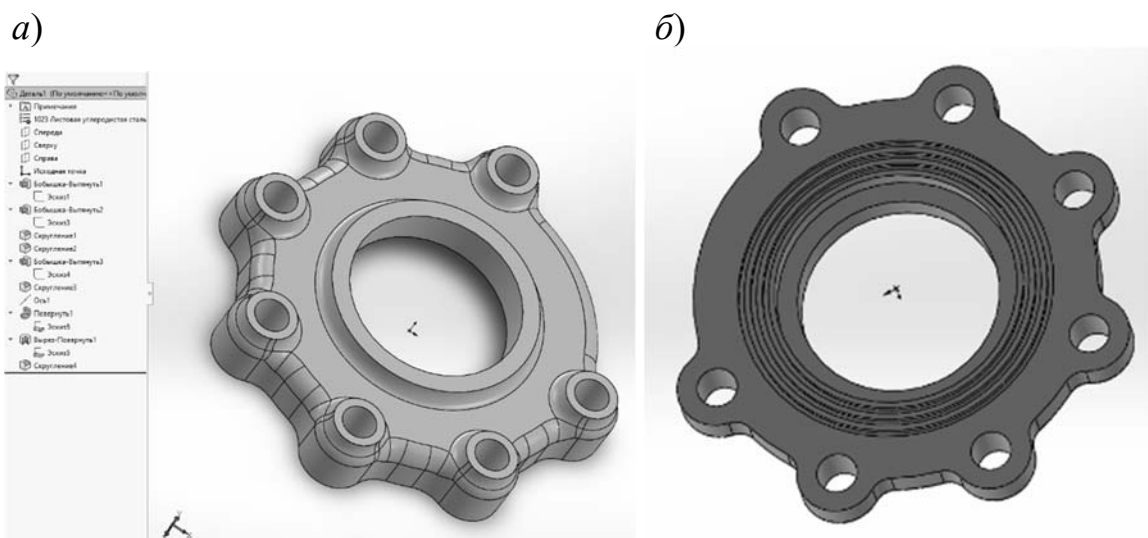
Окончательный вид детали (а) и обратная сторона фланца (б)
